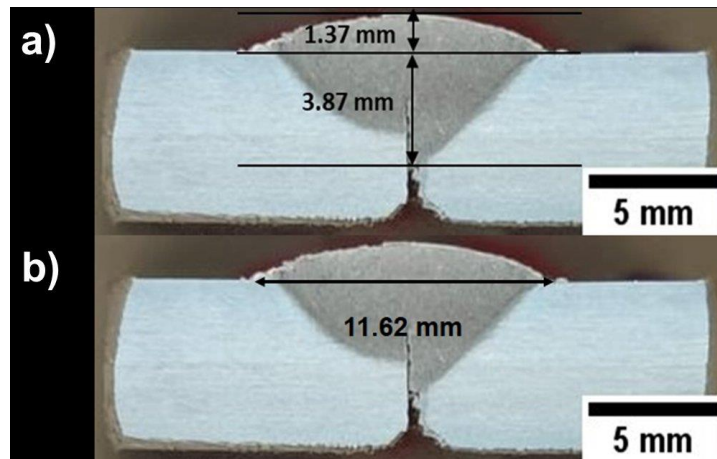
82 Geometría del cordón de soldadura número 17, cuyos valores son a) 1.37 mm de concavidad de la corona y 3.87 mm de penetración y b) 11.62 mm de ancho del cordón de soldadura.
